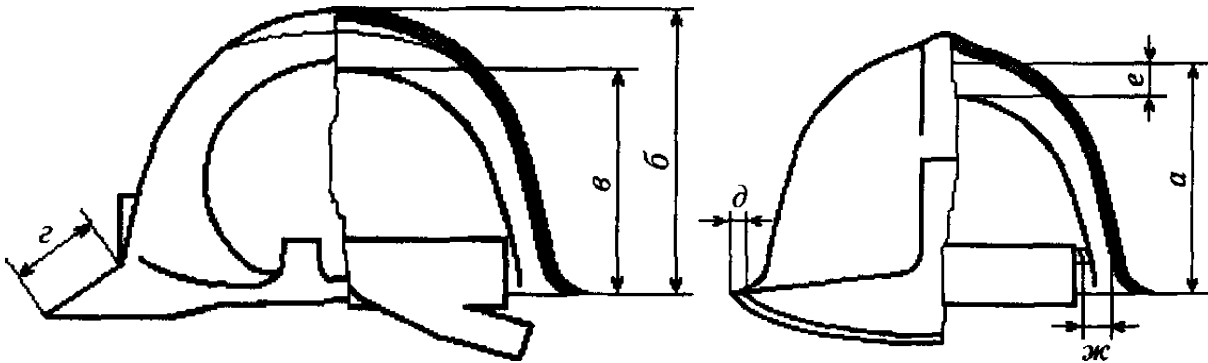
Корпус шахтерской каски: а – высота корпуса без учета ребра жесткости; б – высота корпуса с ребром жесткости; в – глубина внутренней оснастки; г – ширина козырька; д – ширина полей; е – вертикальный безопасный зазор; ж – кольцевой зазор
